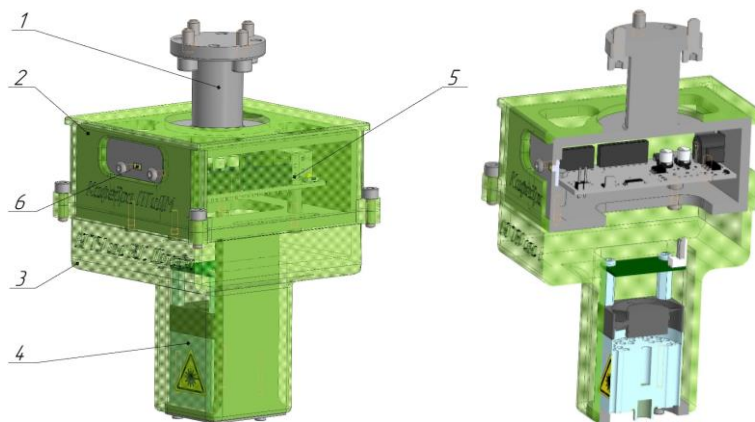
Разрез и комплектность измерительно-разметочного устройства: 1 – основание; 2- крышка верхняя; 3 – крышка нижняя; 4 – лазер; 5 – микропроцессор; 6 – лазерный дальномер
